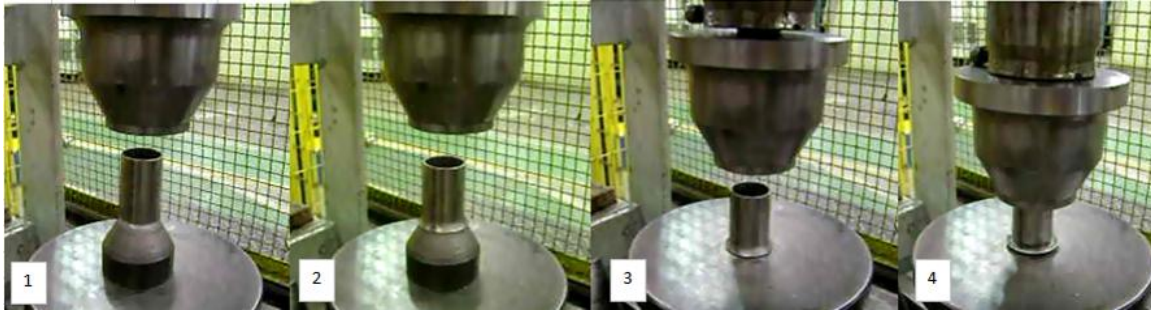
Ensaio de flangeamento. [1] Posicionamento para pré expansão com cone de 60°, [2] Realização da pré expansão, [3] antes do flangeamento e [4] após ensaio de flangeamento. Fonte: Autor.
